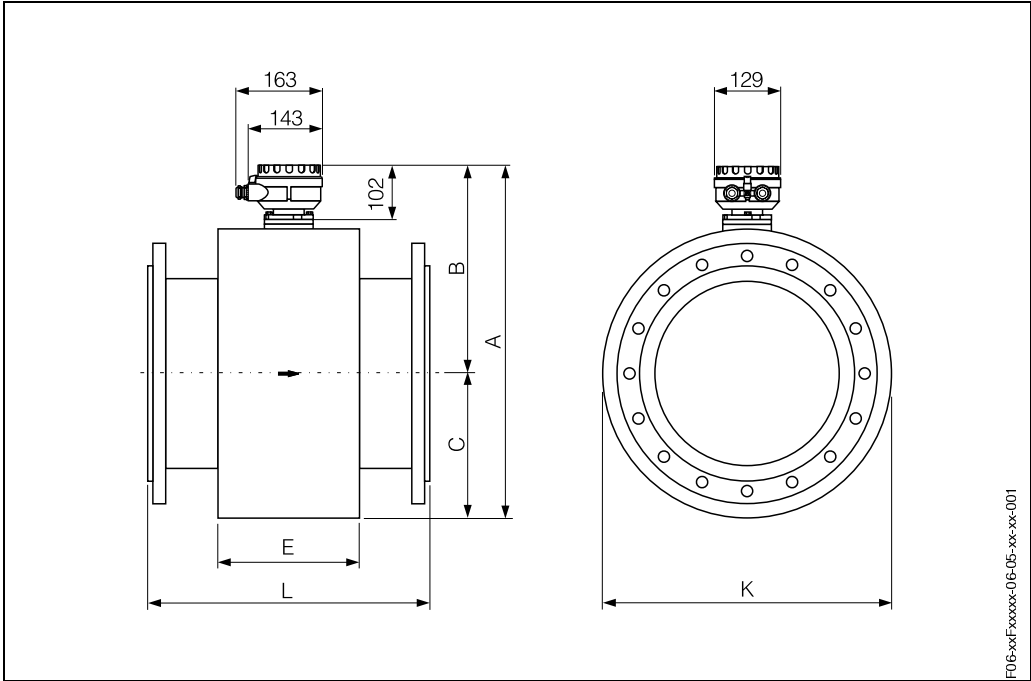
Dimensiones del Promag P / DN ≥ 350 (versión separada)
